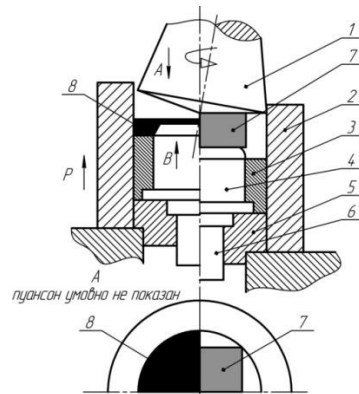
Схема наладки для штампування обкочуванням з квадратної заготовки фланцевих деталей: 1 - пуансон; 2 - контейнер; 3, 4 матриця; 5 - кільце; 6 - виштовхувач; 7 - вихідна заготовка; 8 - готова деталь.
